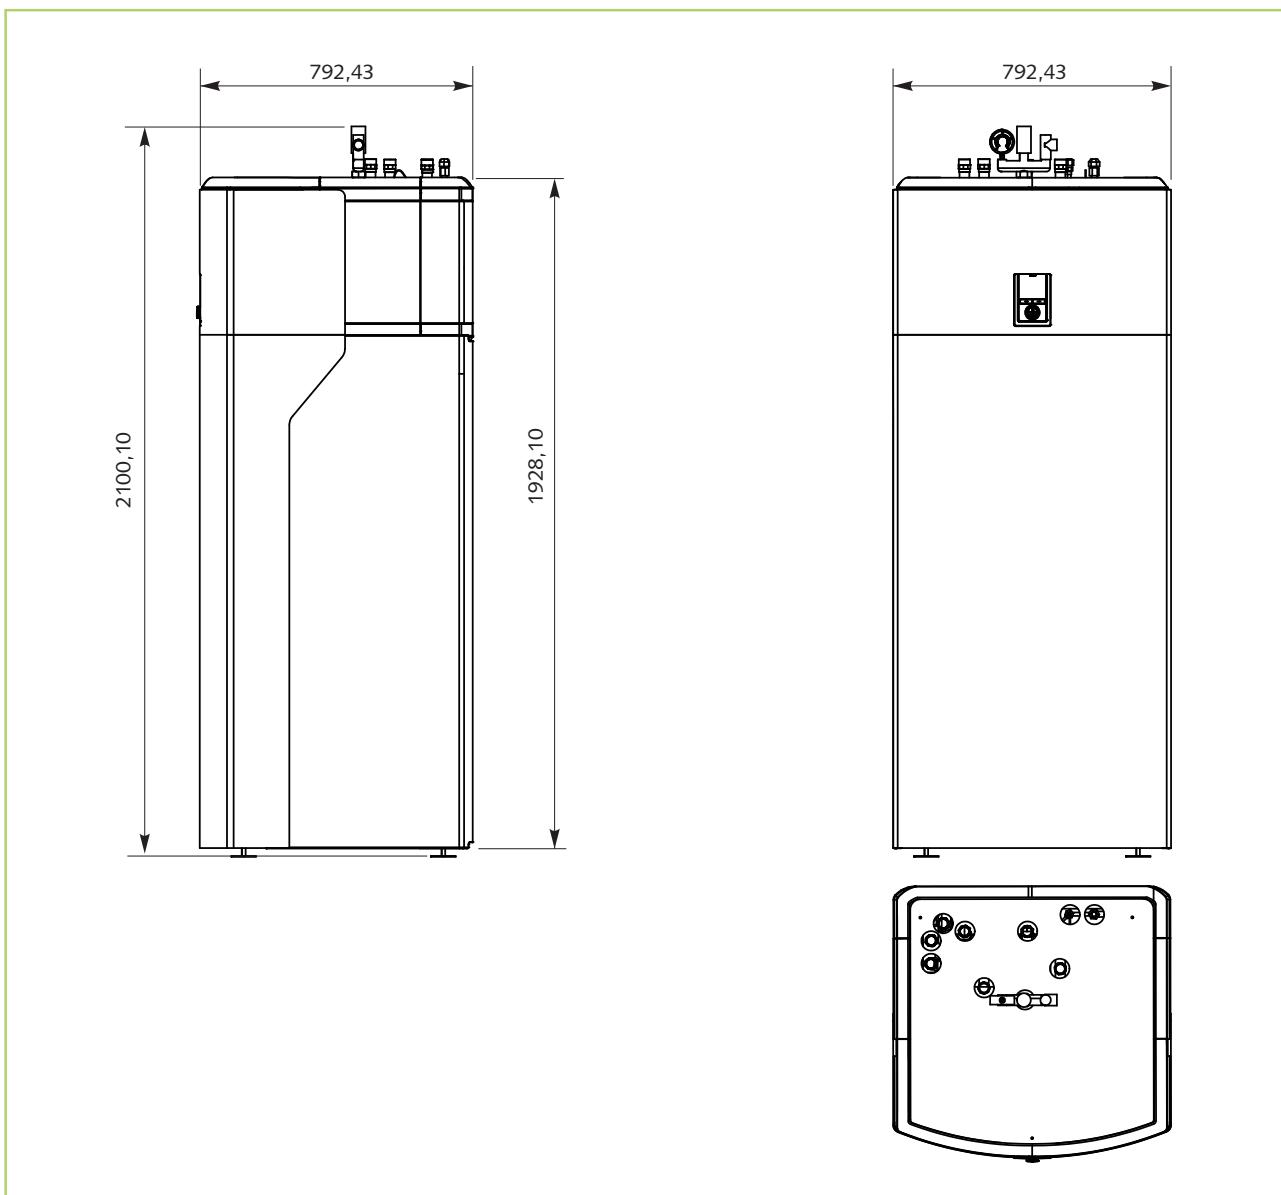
Abmessungen Innenmodule WKF-compact 85/120/180 (Alle Maße in mm)
